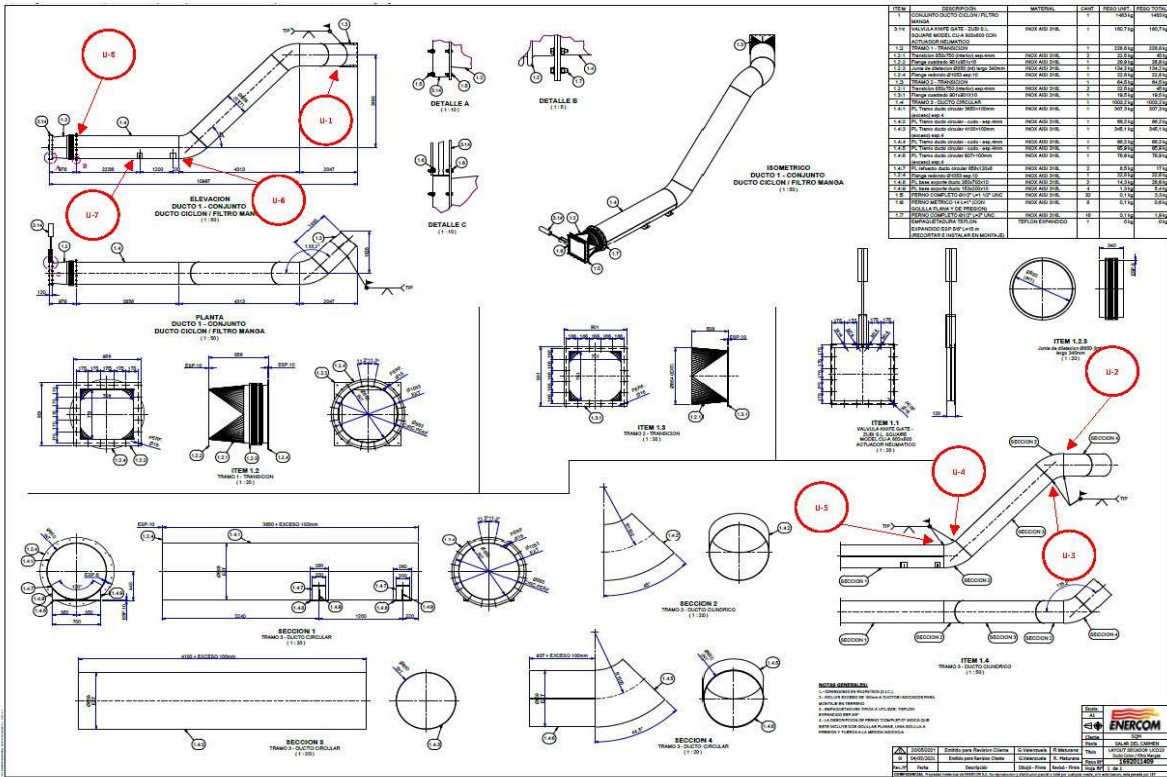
, Mapeo Plano 1692011409-DUC FM 1\_R1 modificado
